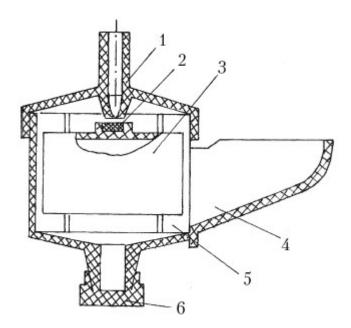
Поплавковая поилка: 1 – отверстие в крышке; 2 – резиновый клапан; 3 – поплавок; 4 – чаша; 5 – поплавковая камера; 6 – сливная пробка
